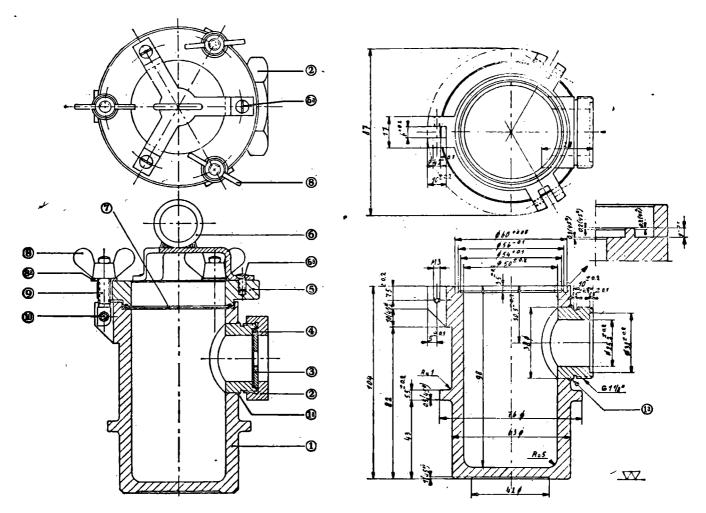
Recipiente a presión montado (vistas esquemáticas en sección vertical y en planta)
